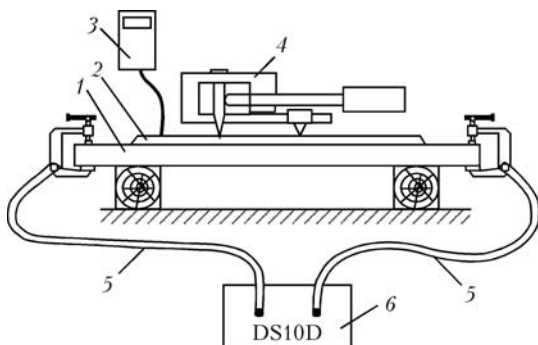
Схема проведения ЭФО с изучением характера деформирования образца: 1 — обрабатываемый образец; 2 — шов; 3 — мультиметр; 4 — деформометр; 5 — кабели; 6 — установка для ЭФО
